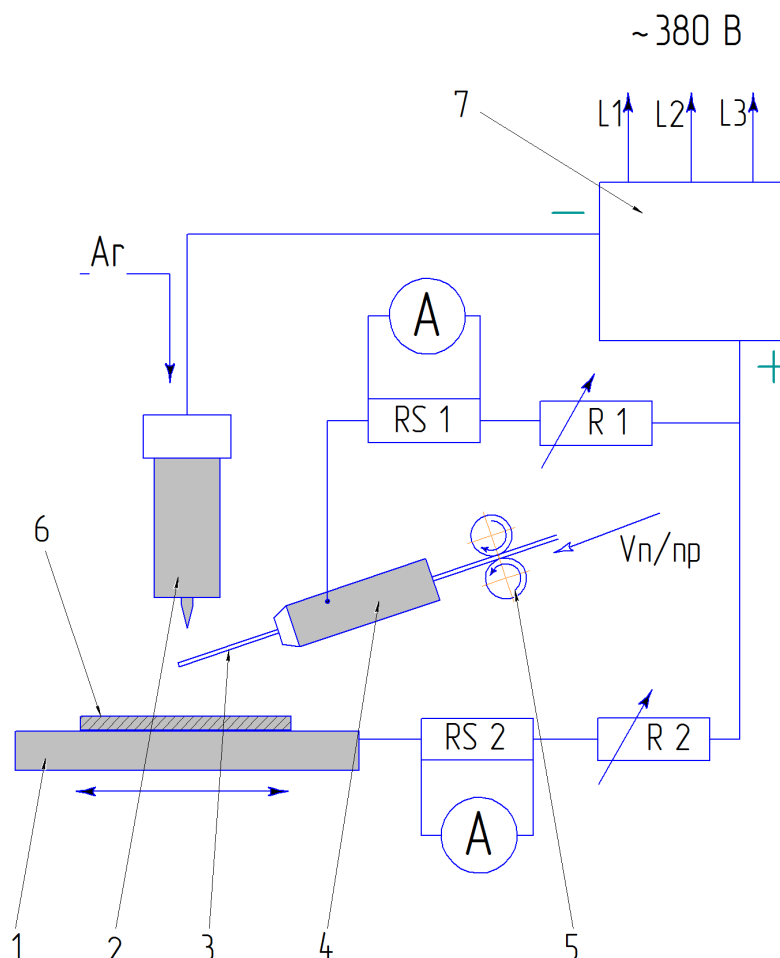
Схема питания комбинации дуг при сварке плоских деталей: 1 – перемещающаяся каретка; 2 – аргонодуговая горелка; 3- присадочная проволока; 4- горелка для полуавтоматической сварки; 5 – подающий механизм; 6 – образец для наплавки
